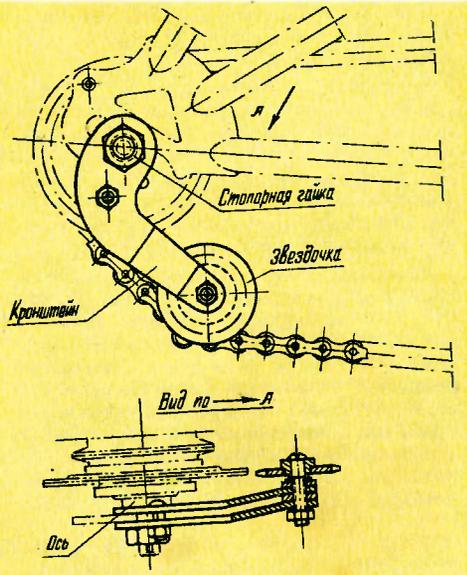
Устройство для регулировки натяжной цепи ножного привода.
